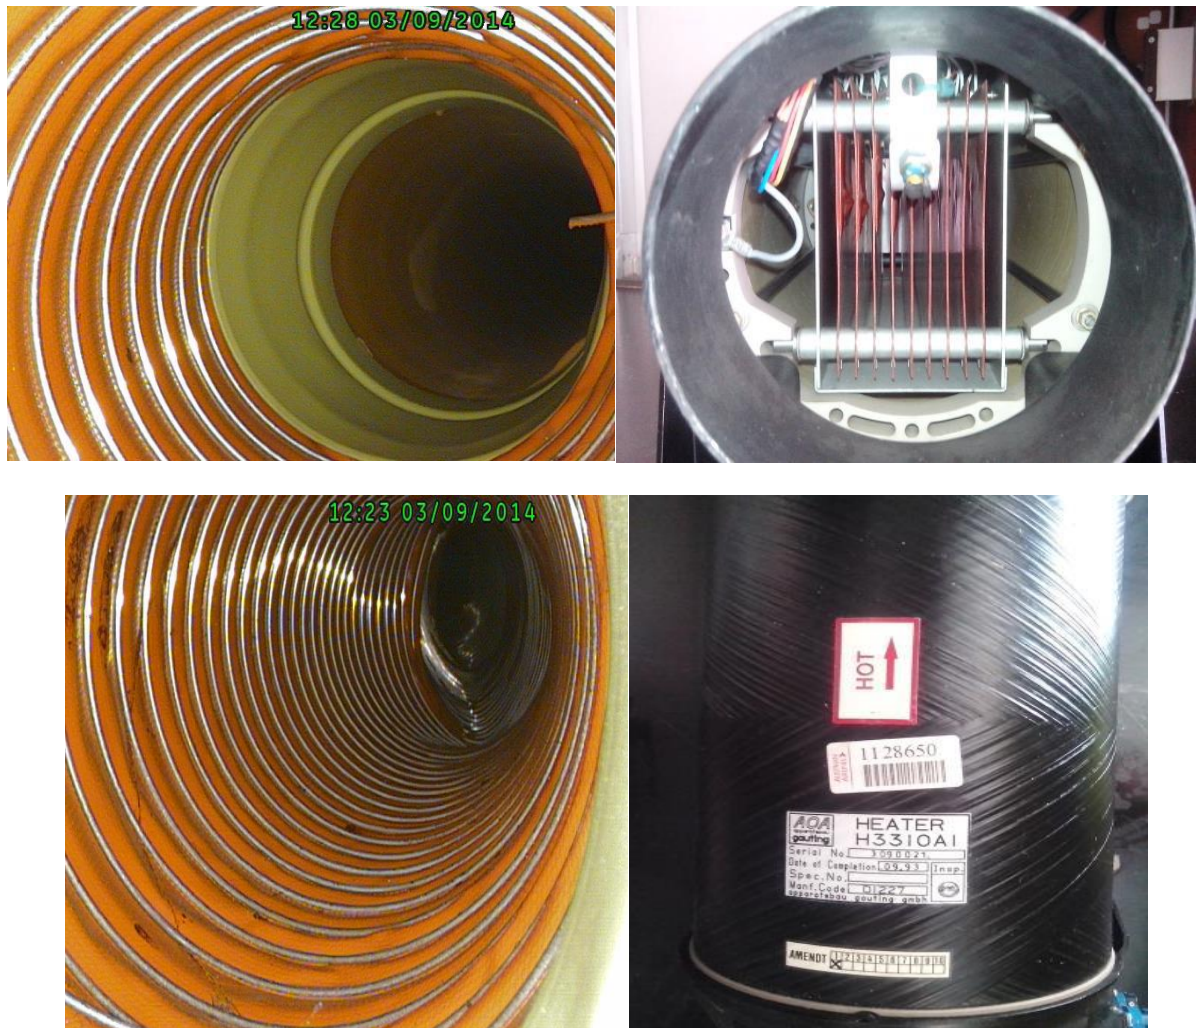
Inspeção Boroscópica e Componentes removidos
